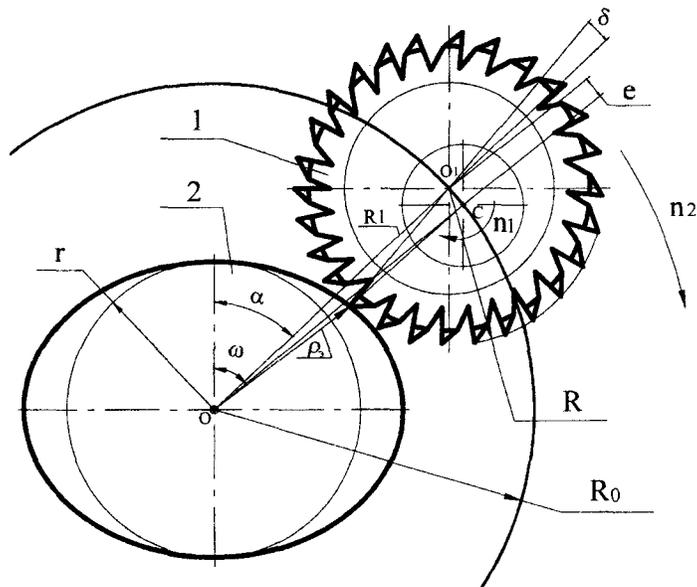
Схема обработки профильного вала дисковой эксцентрично установленной фрезой:
